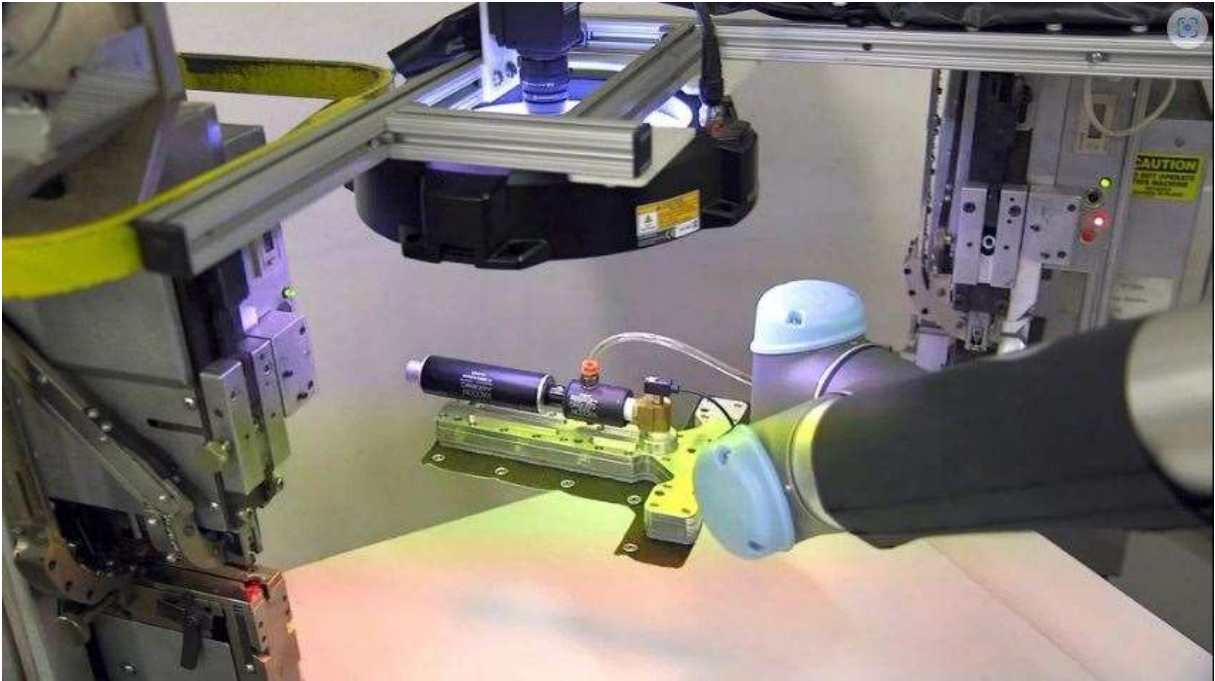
Inspección. Fuente: Universal Robots (Universal Robots, 2019).
